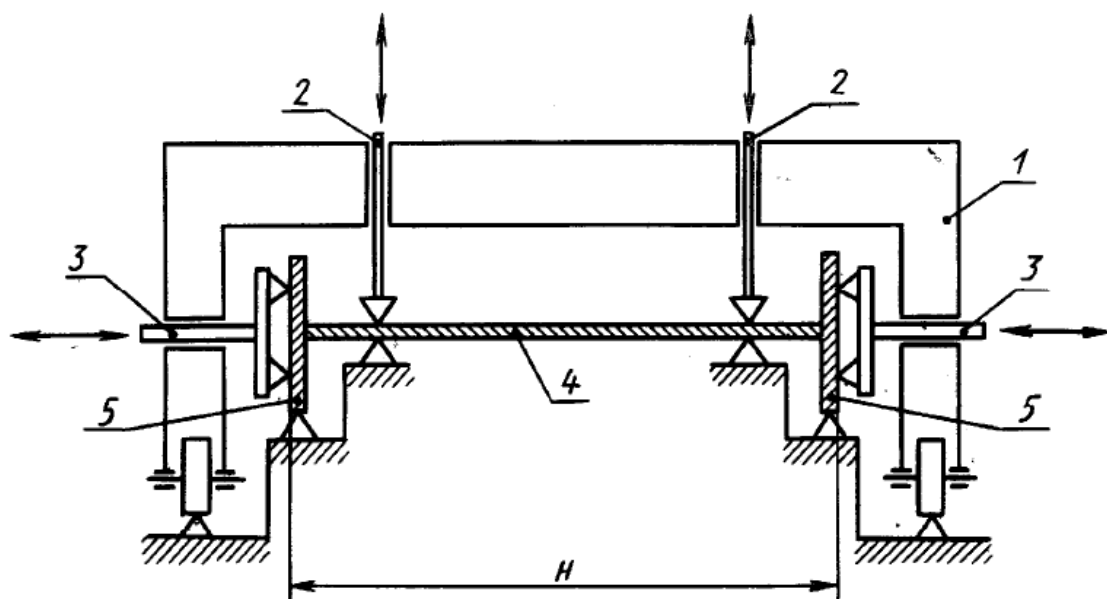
Схема самоходного портала для сборки двутавровых балок
